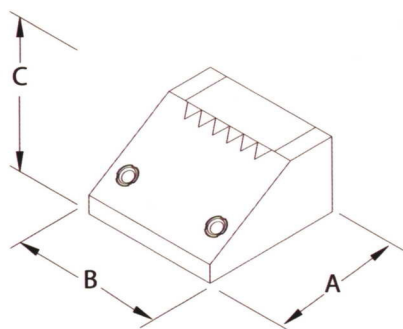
Размеры призмы: А – длина; В – ширина; С – высота
